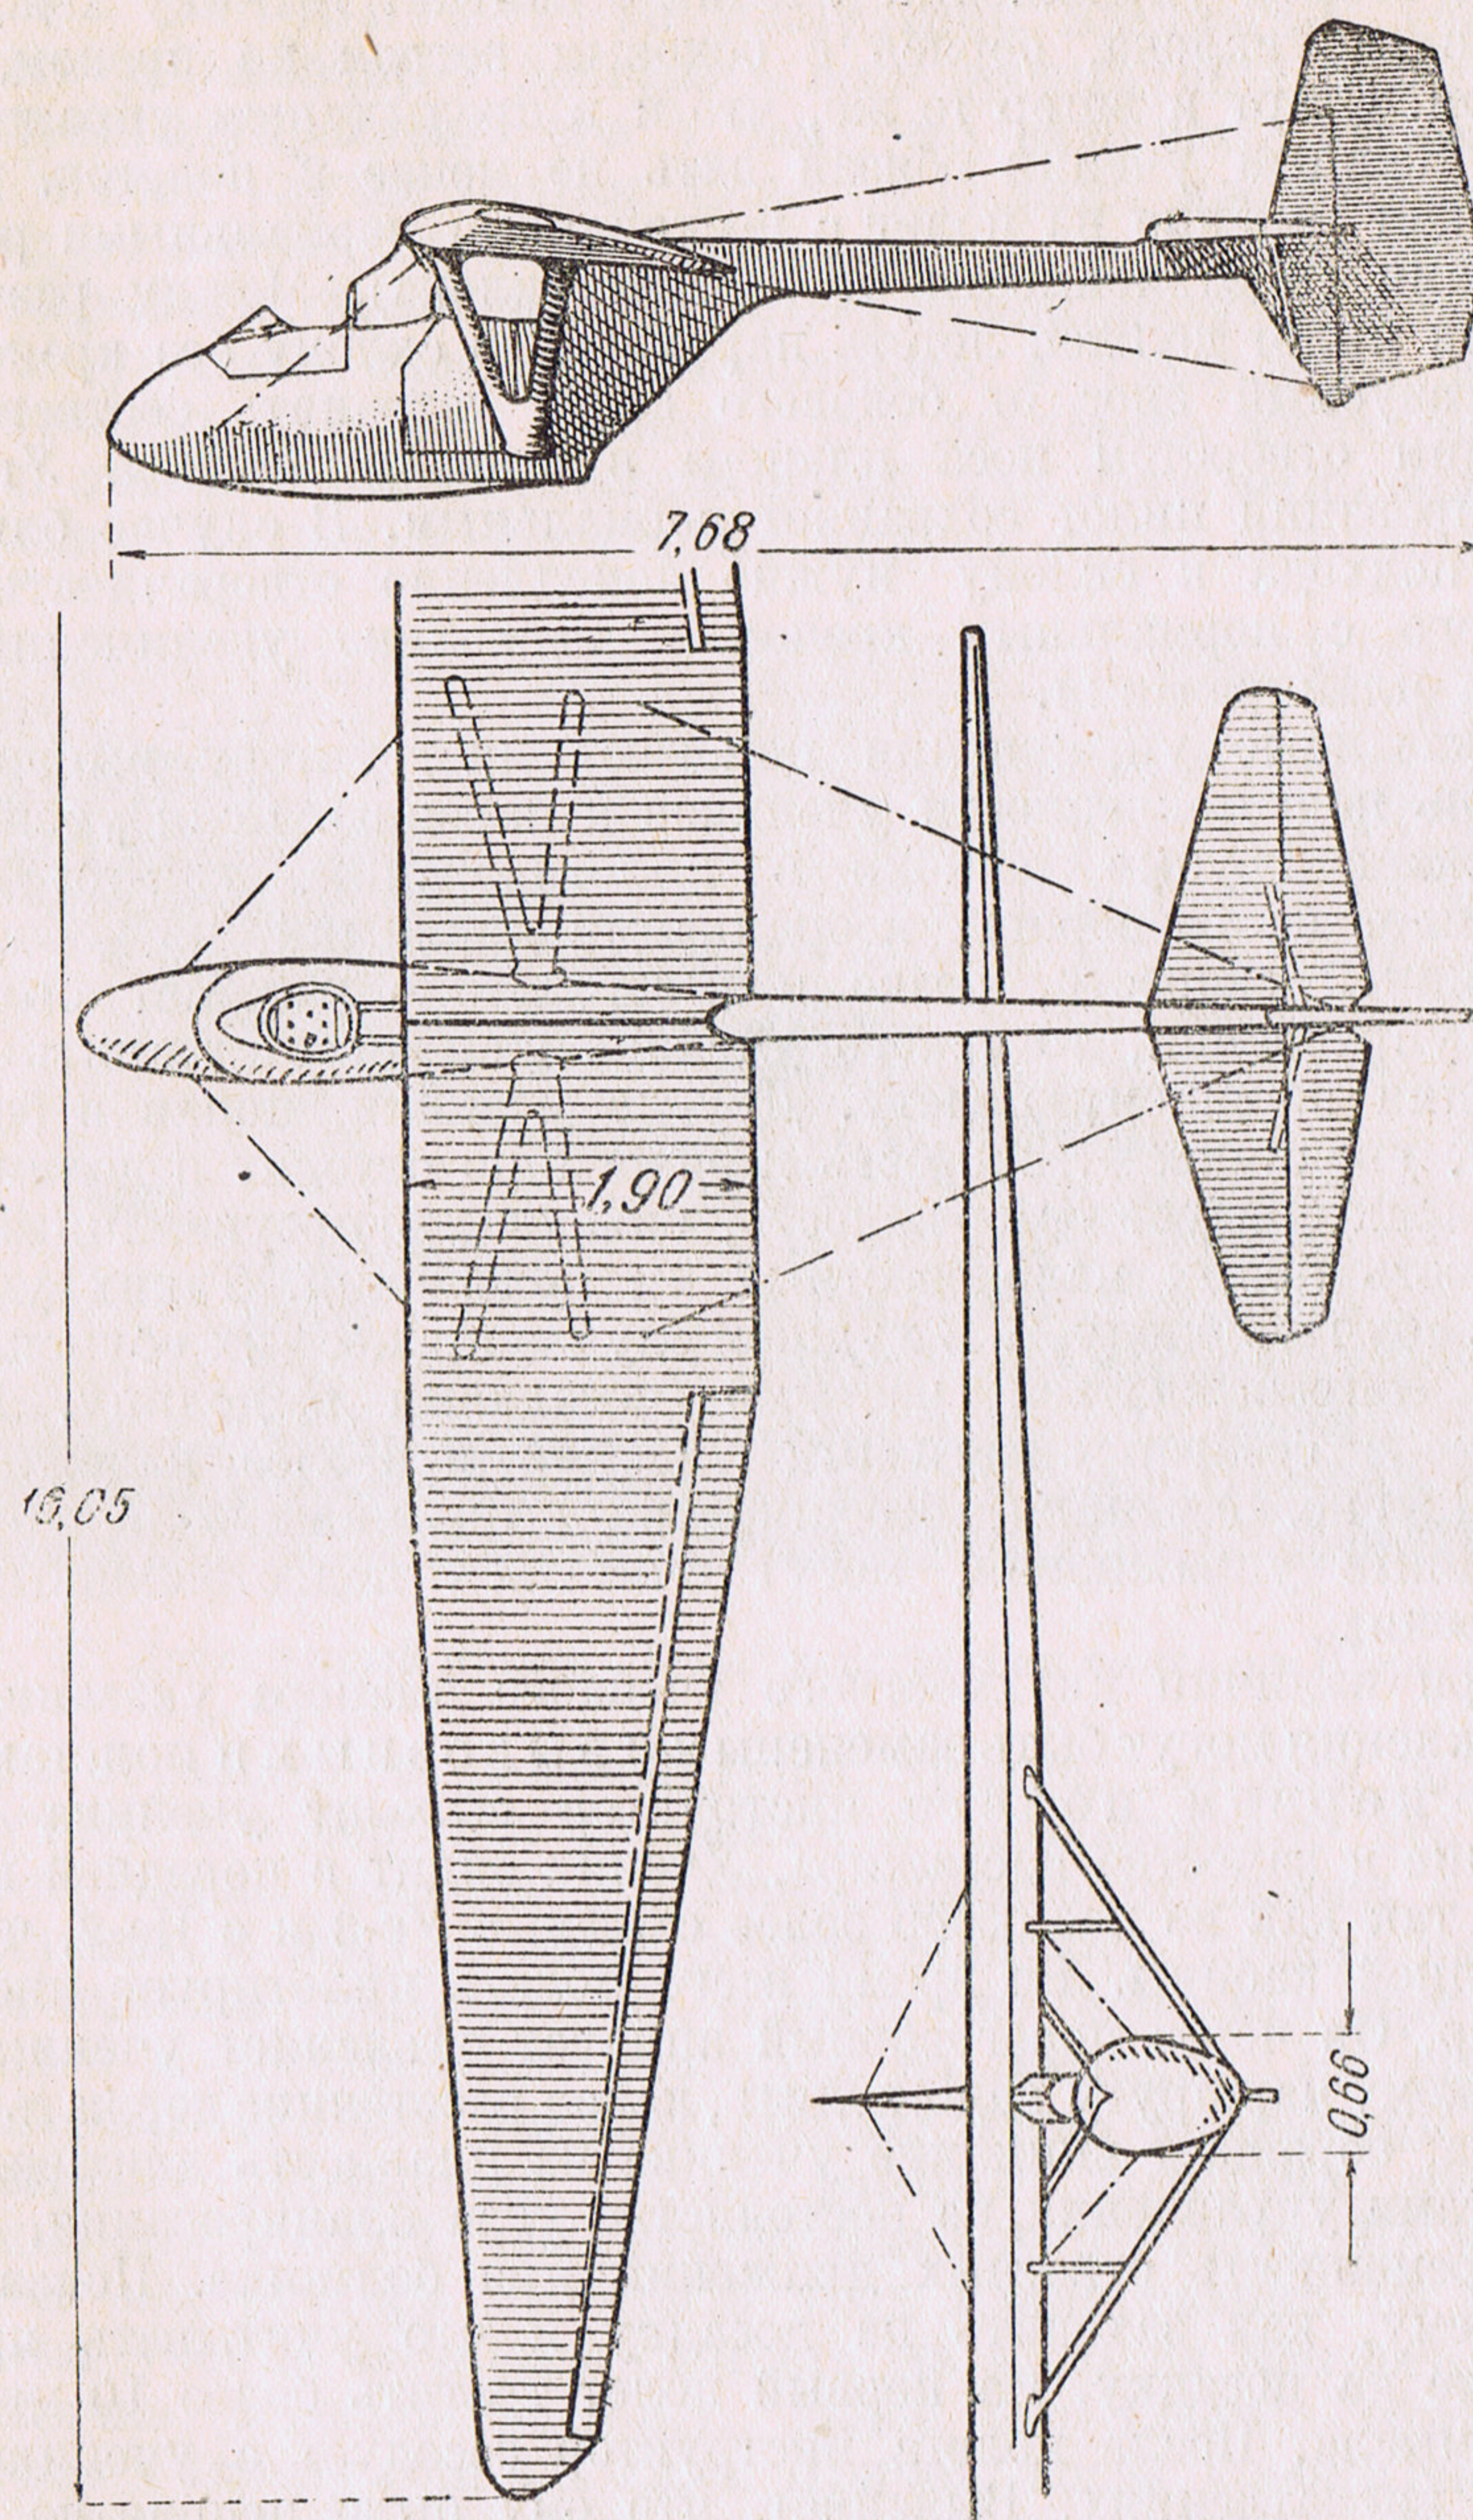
Схема планера П-5 конструкции инженера Шереметьева.
